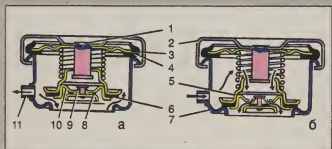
Крышка радиатора. а – открыт паровой клапан; б – открыт воздушный клапан; 1 – стойка; 2 – крышка; 3 – запорная пружина; 4 – уплотнитель; 5 – паровой клапан; 6 – прокладка парового клапана; 7 – горловина радиатора; 8 – прокладка воздушного клапана; 9 – пружина воздушного клапана; 10 – седло воздушного клапана; 11 – трубка к расширительному бачку.
